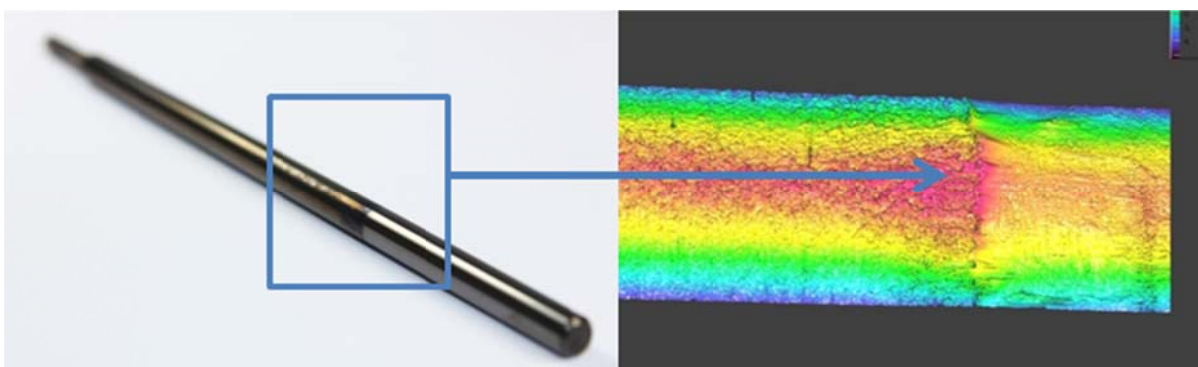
3D-Mikroskopische Aufnahme eines Steuerkolbens
